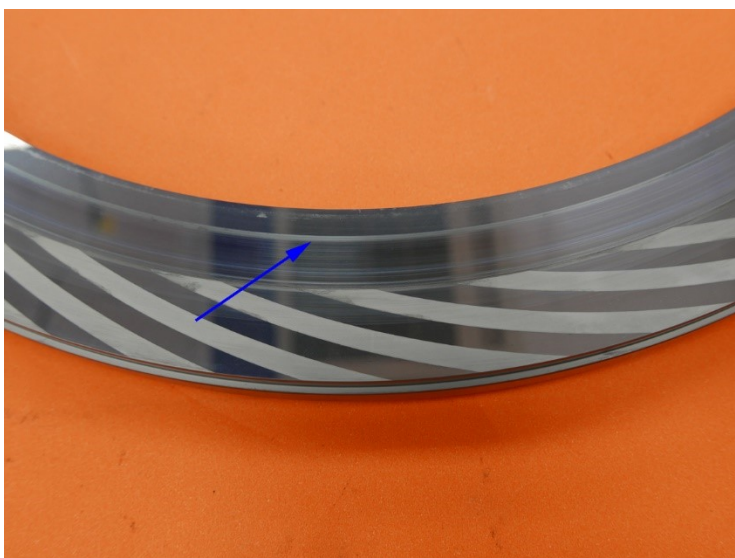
Sedlo poškozené explozivní dekompresí
